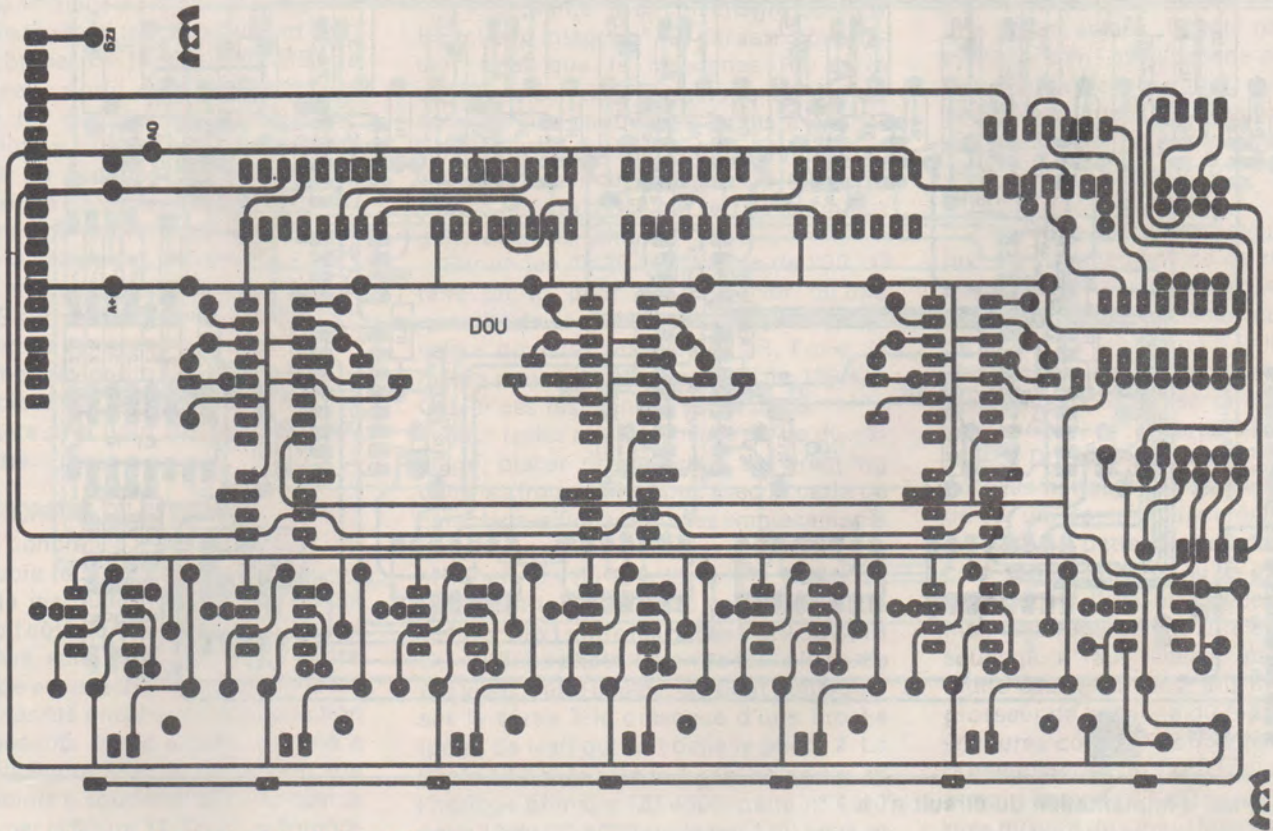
Circuit imprimé n° 1 côté soudures.
